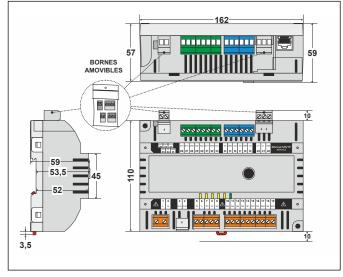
Dimensions du PCD7.LRSx (en mm)
